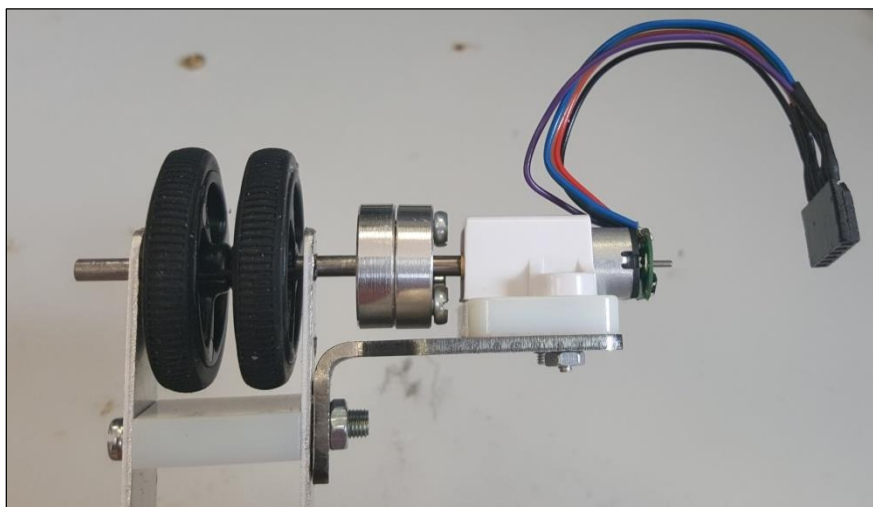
Montaje Soporte Motor – Placa Motor
